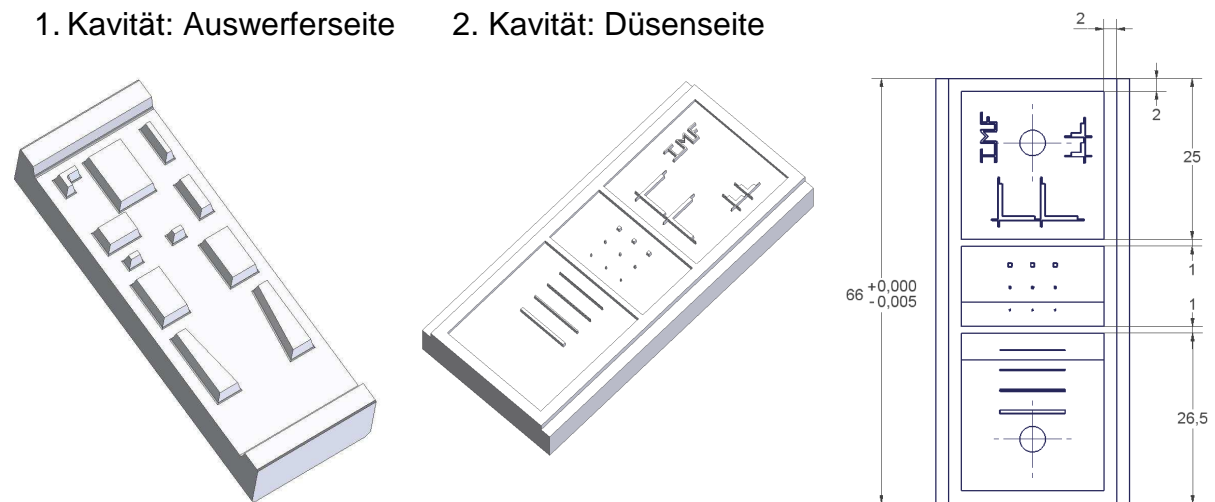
Formeinsätze für das 2K-Indexplatten-Werkzeug
